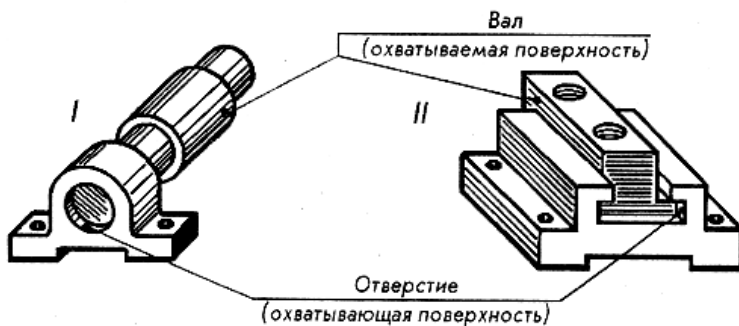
Охватывающие и охватываемые поверхности деталей
